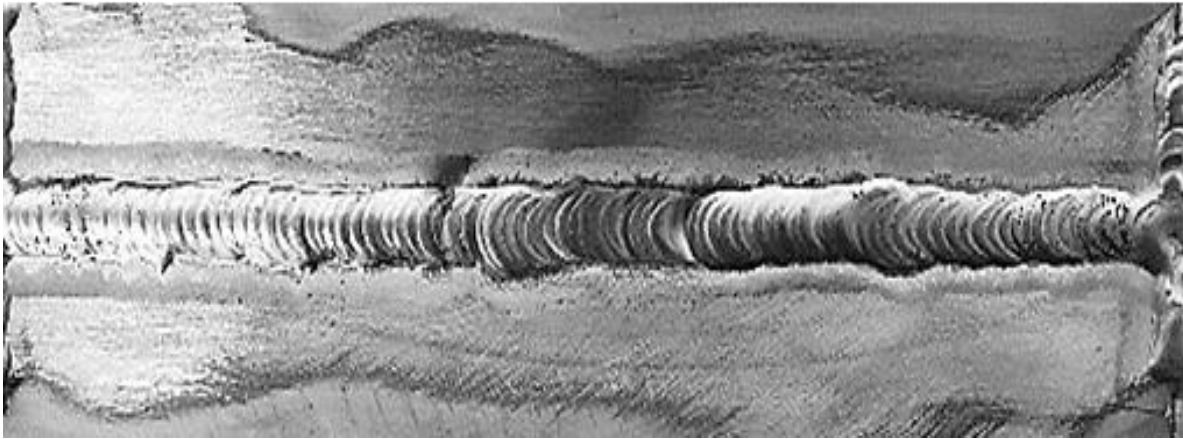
Porosidades en el cordón de soldadura con material de aporte
